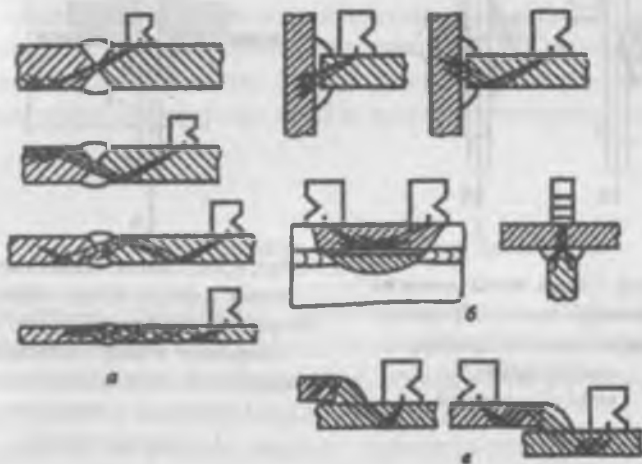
Схемы испытания швов сварных соединений.
